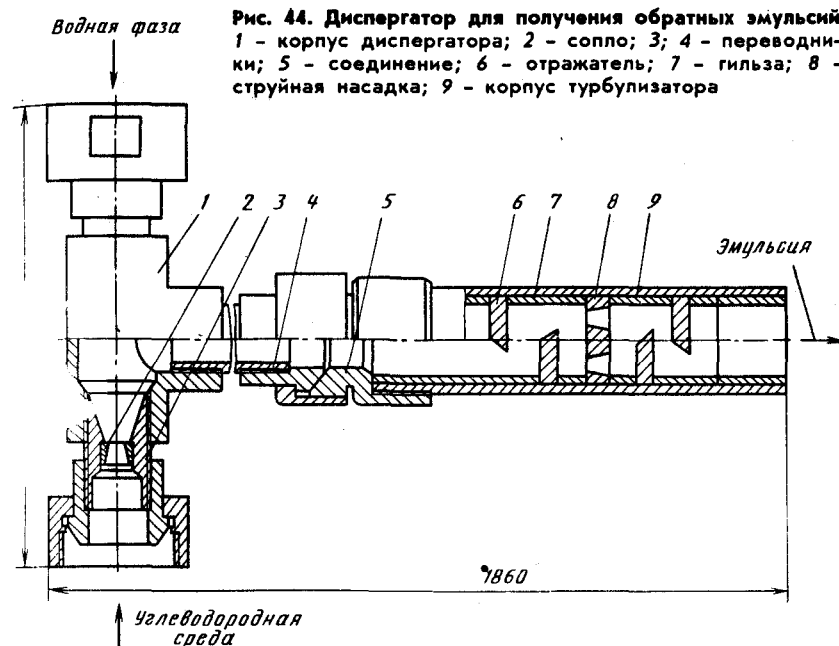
Диспергатор для получения обратных эмульсий: 1 - корпус диспергатора; 2 - сопло; 3, 4 - переходники; 5 - соединение; 6 - отражатель; 7 - гильза; 8 - струйная насадка; 9 - корпус турбулизатора
